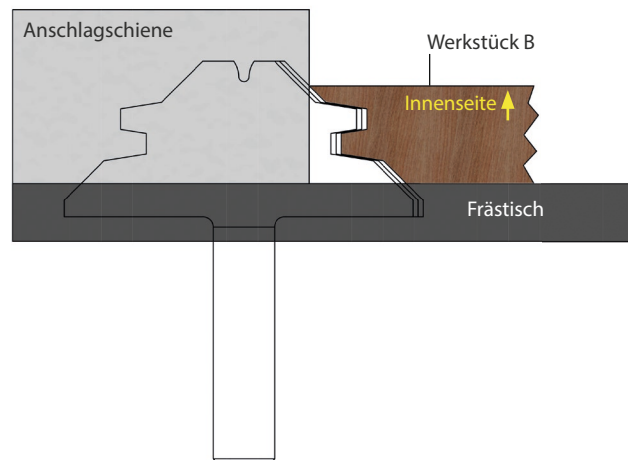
Fräsen des Werkstücks B mit der Innenseite nach oben.
